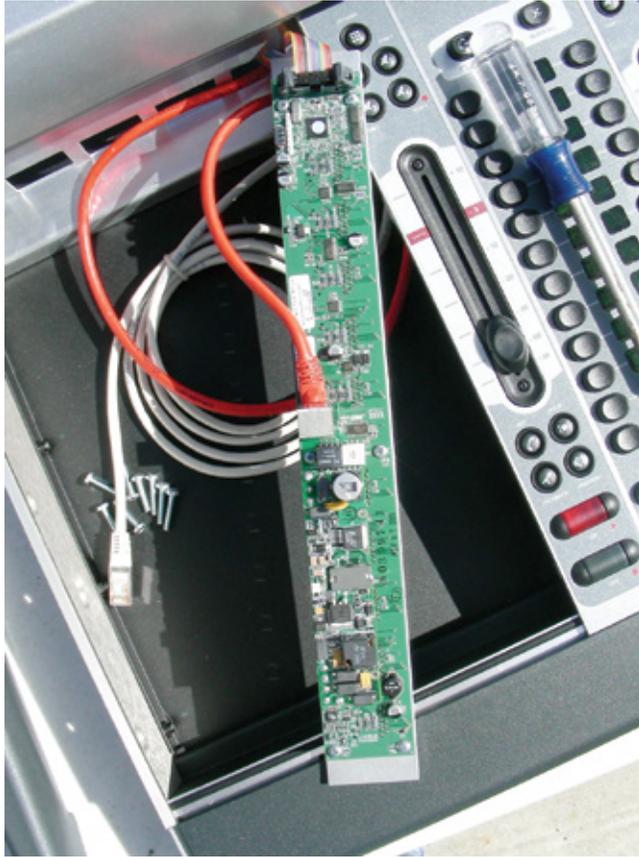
Vista en reversa del modulo conectado. Observe el cable plano conectado con la parte trasera hacia arriba
